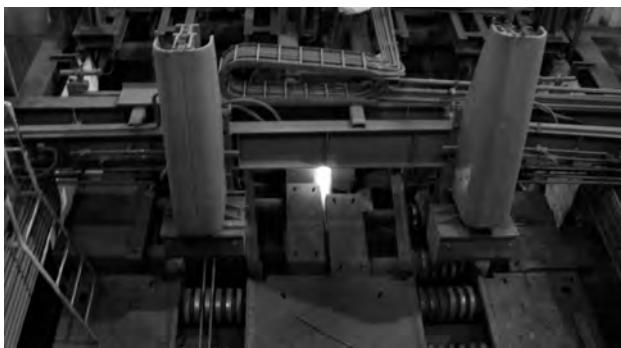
Установка для кислородной резки горизонтально расположенных непрерывно литых слитков (УНРС)
